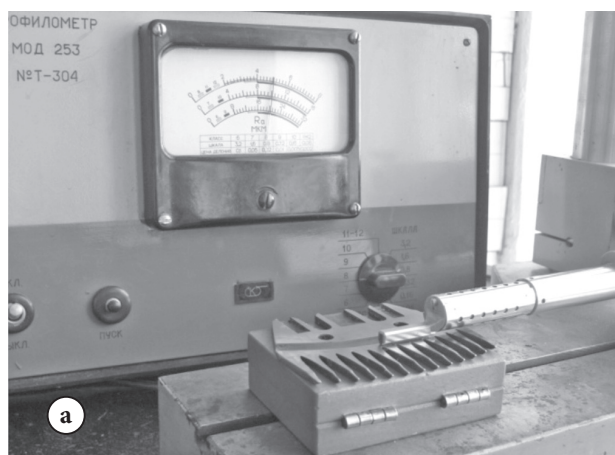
а) измерение шероховатости рабочей поверхности гребёнки;
